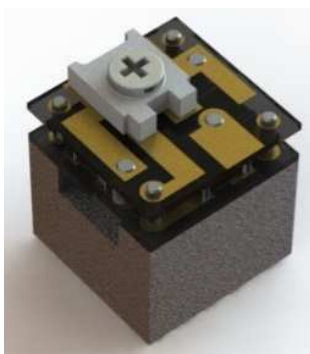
3-D модель миниатюрной сборочной единицы стабилизатора напряжений
